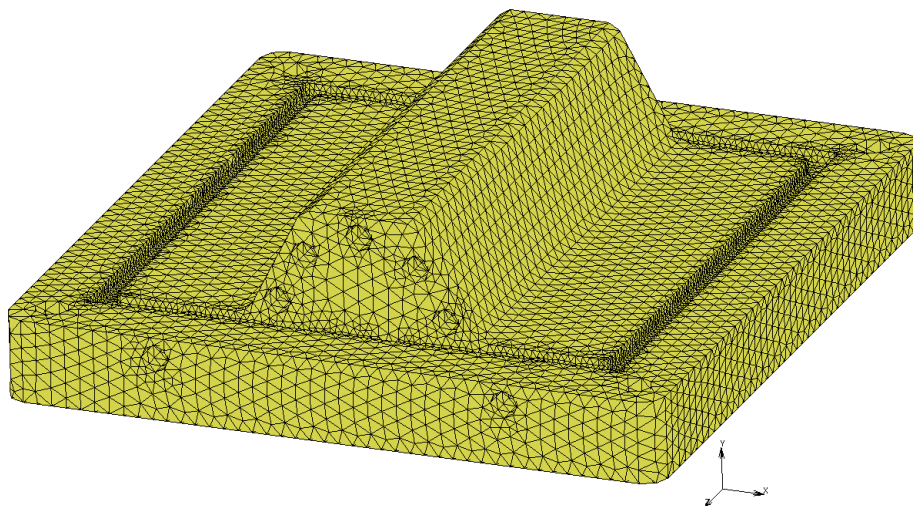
Mallado inicial del molde en 3 dimensiones
